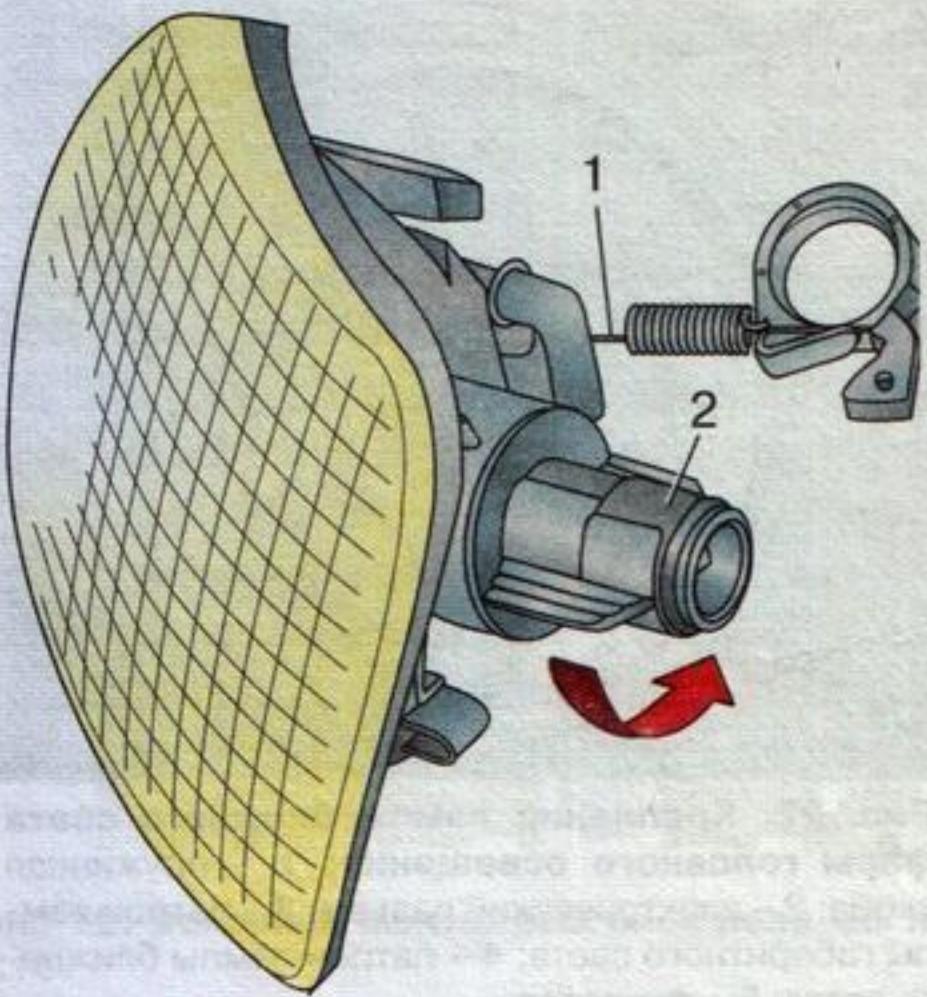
Передний указатель поворота: 1 – трос блокировки крепления указателя поворота; 2 – патрон лампы указателя поворота
